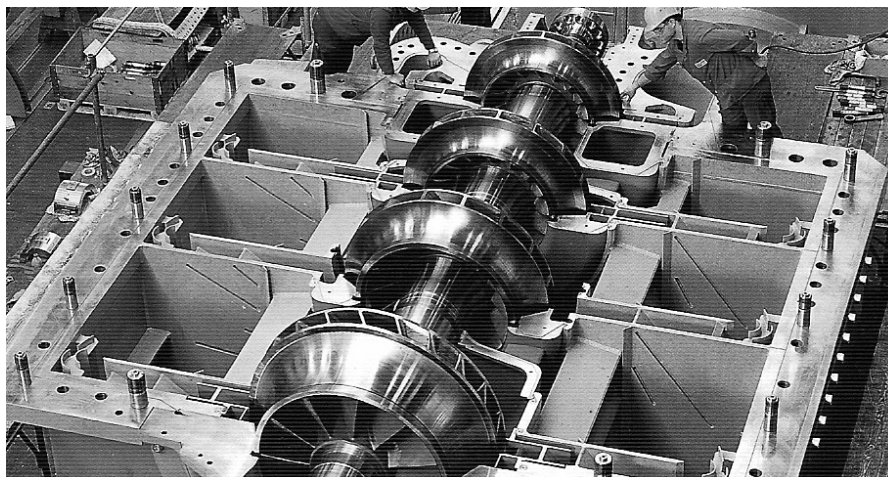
Современный центробежный компрессор с встроенными газоохладителями. Вид на горизонтальный разъем (МАН – ГХХ, Цюрих)
